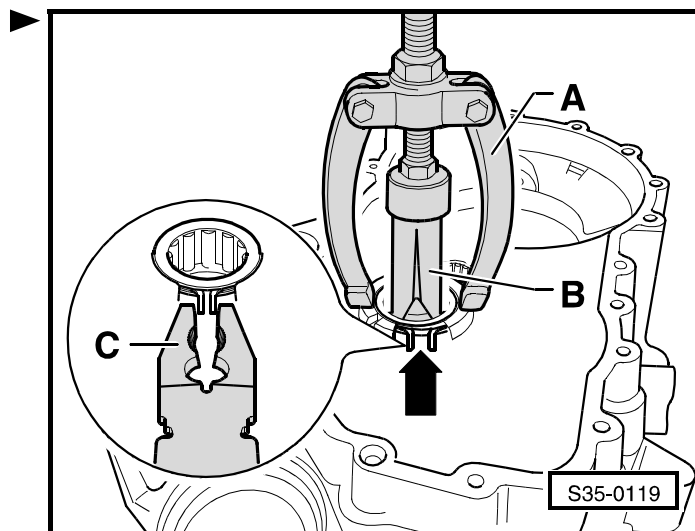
Запрессовывание роликоподшипника в картер сцепления
